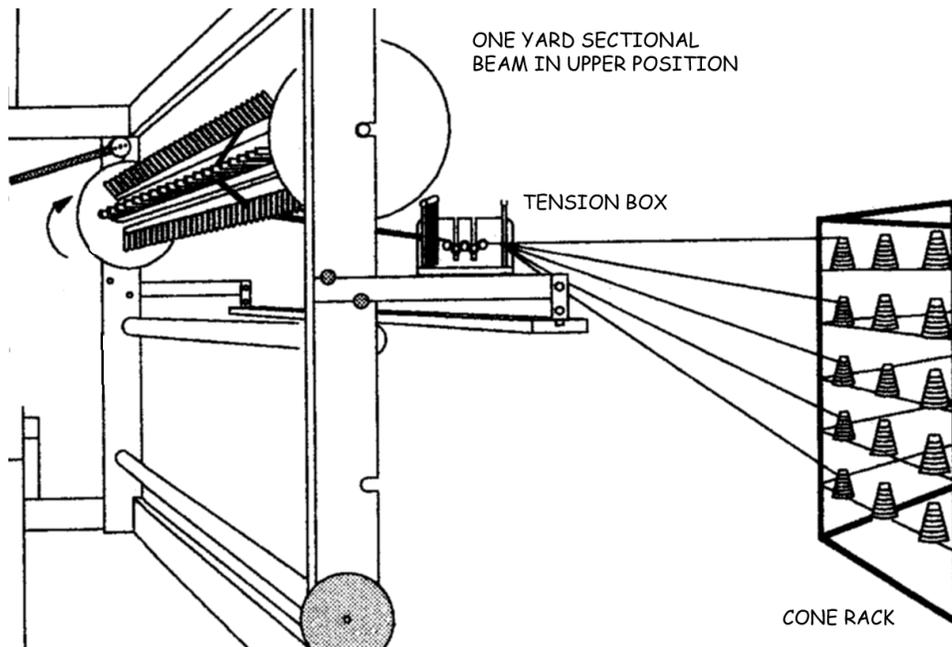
deformación de la viga seccional de un metro en la posición superior
